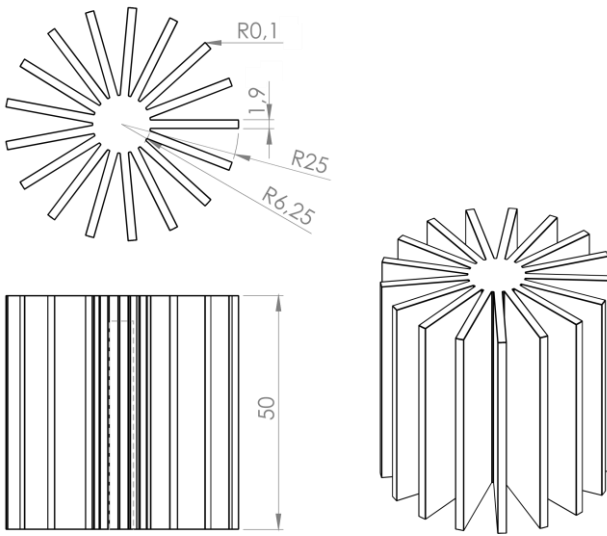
Bemaßte Zeichnung nicht verzweigter zylinderförmiger Kühlkörper
